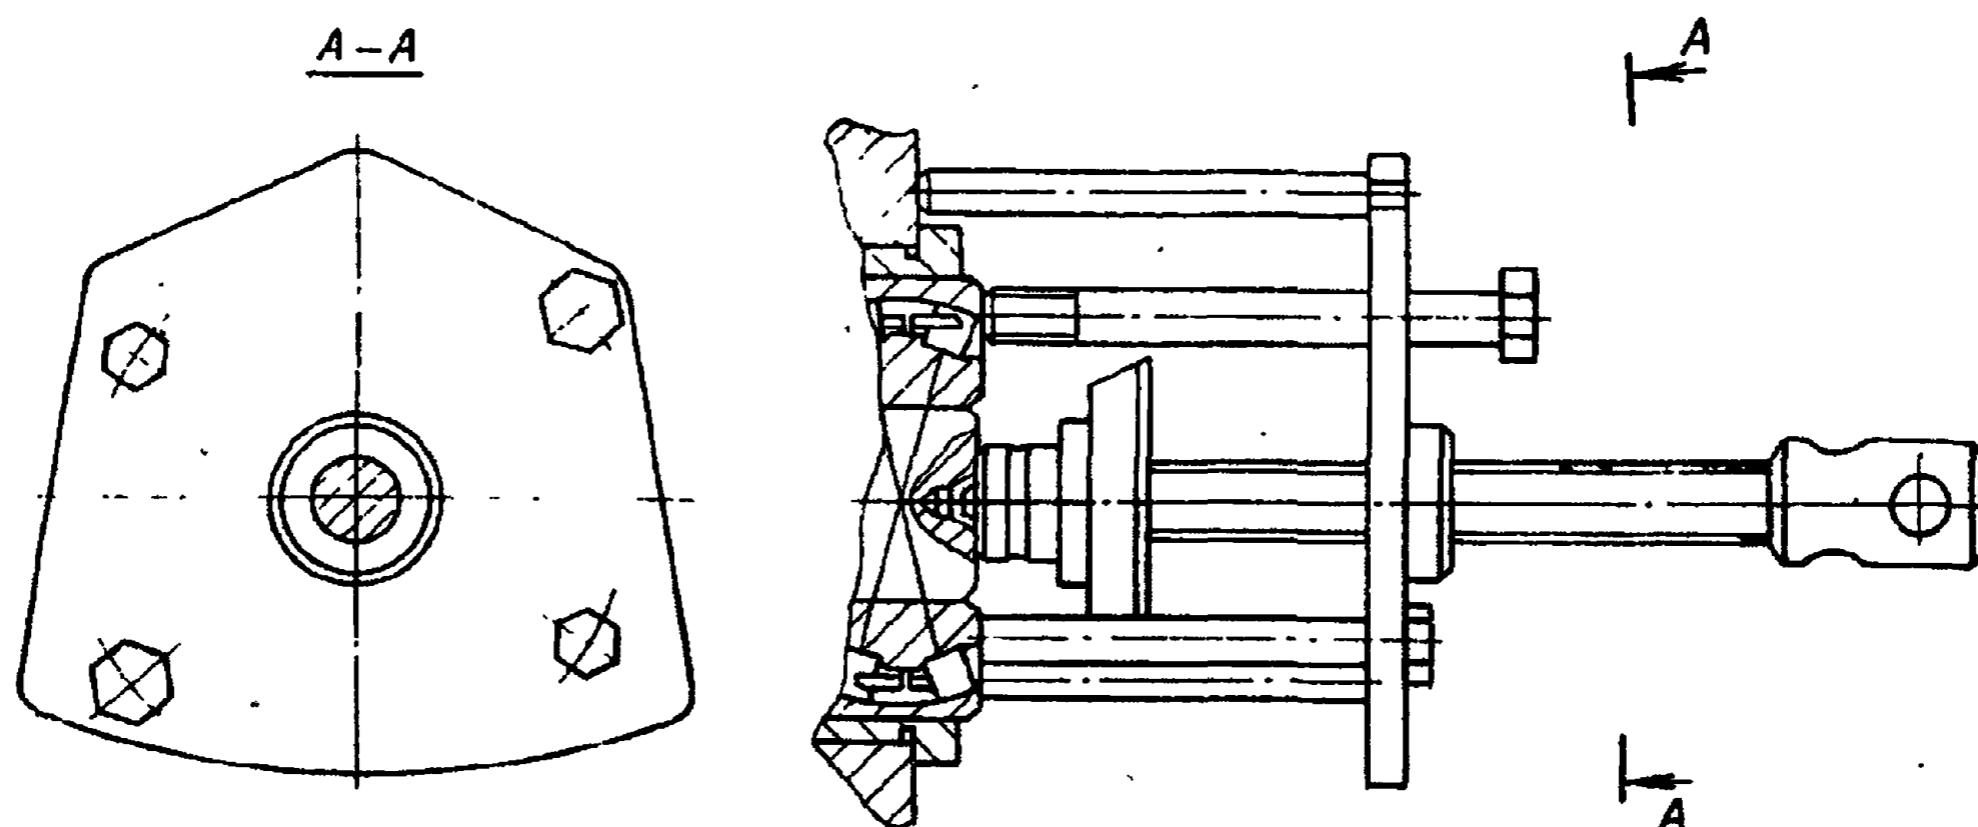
Снятие заднего подшипника ведущего вала со стаканом
